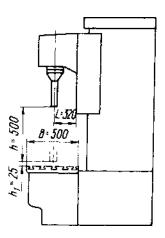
Габаритные размеры рабочего пространства станка модели 2Е78П
